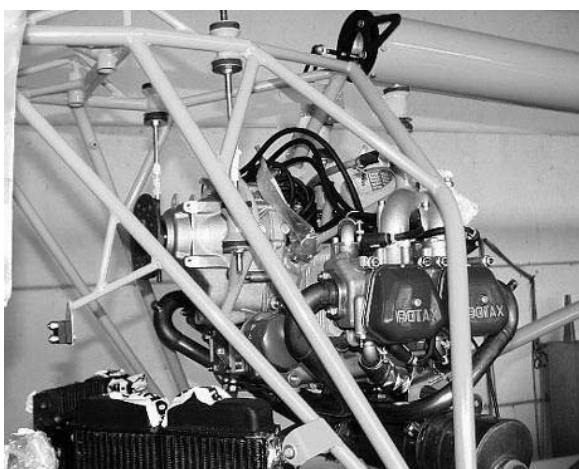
Двигатель Rotax 914 Turbo
